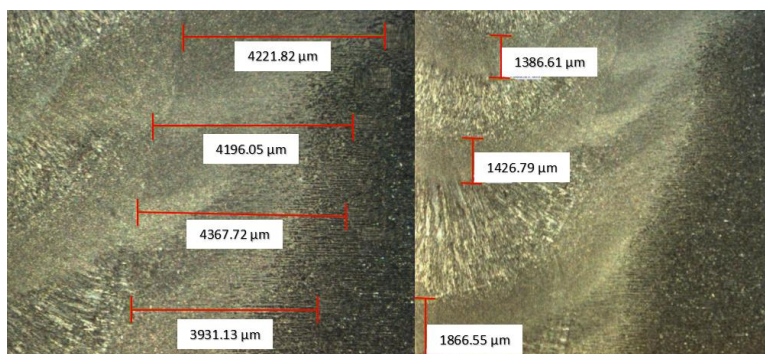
Unión soldada por el proceso FCAW, H.I. = 3.5 KJ/mm. Medición del ancho de la ZAC y de la profundidad del metal de soldadura recristalizado.
